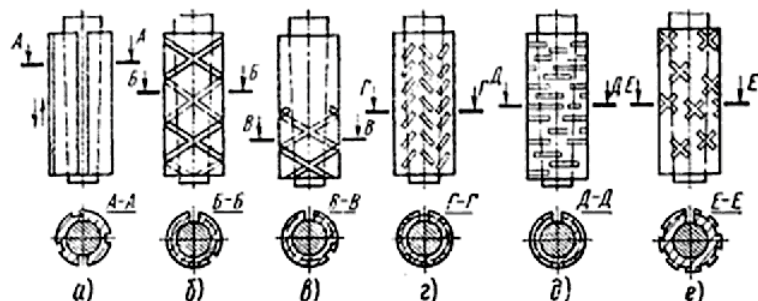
Притиры с различными канавками на рабочей поверхности
